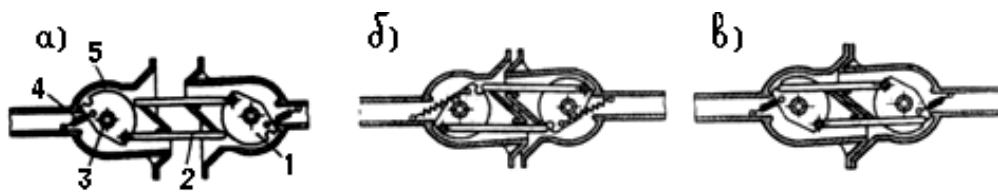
Схеми різних положень зчіпного механізму автозчепу:
